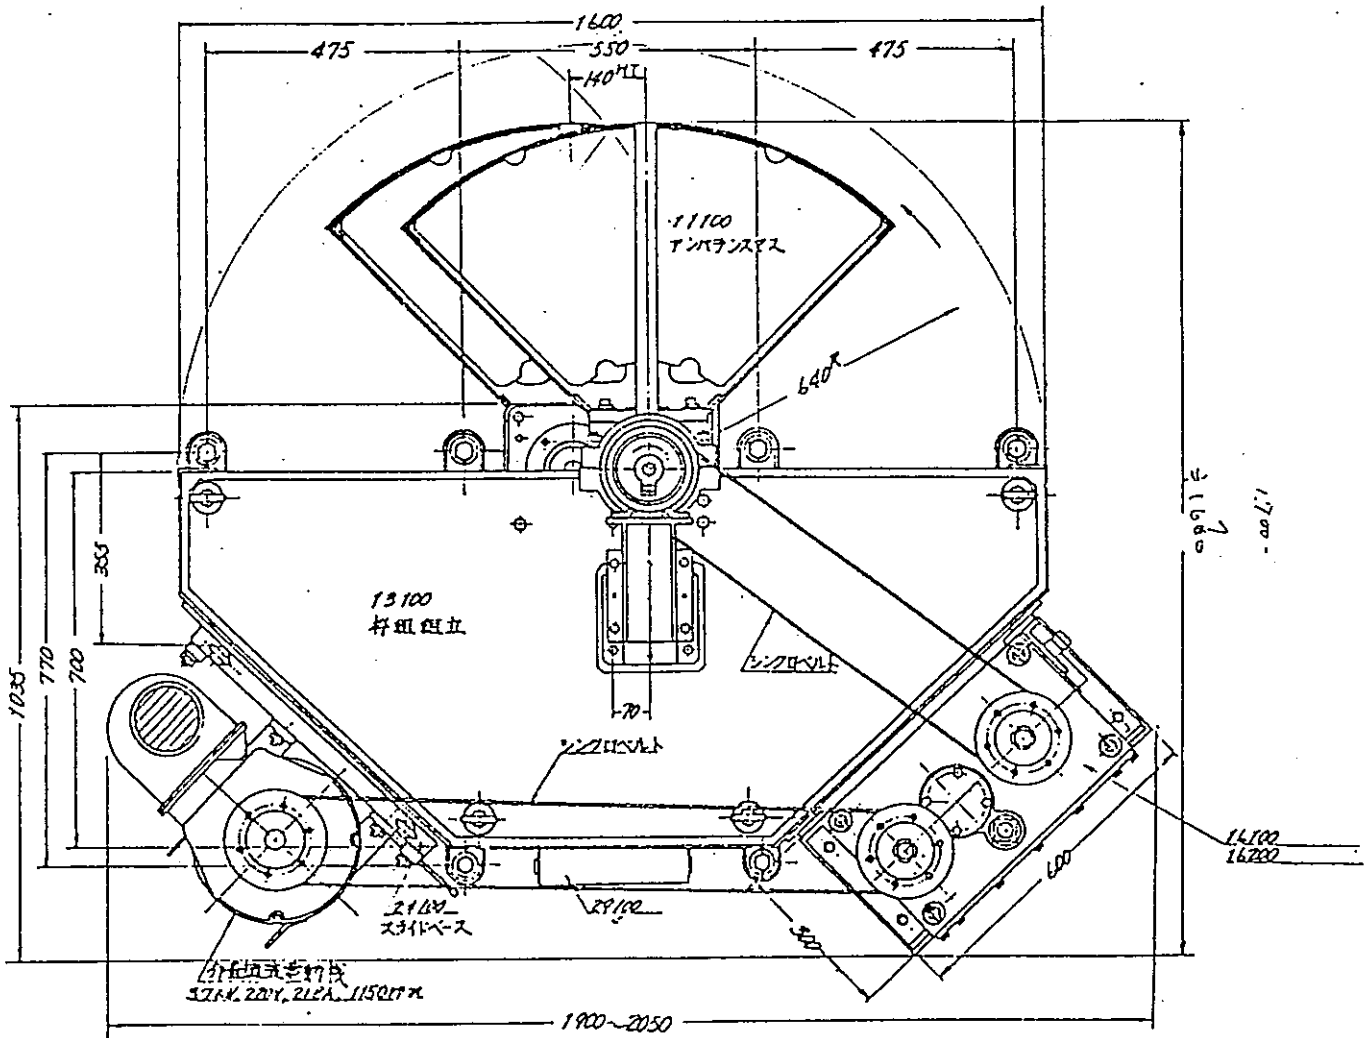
1 起振機形状図 BCS - A 2 0 0 平面図
